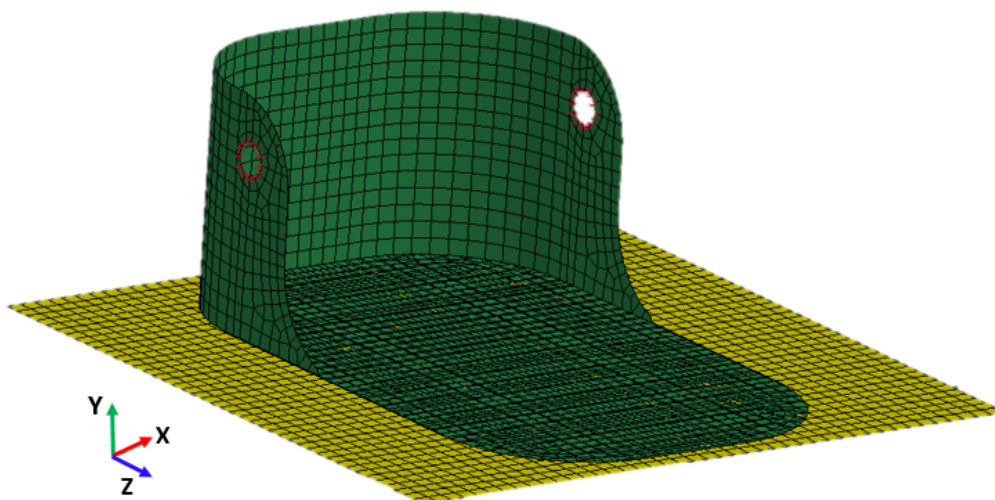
Nós do encastramento destacados a vermelho. Plano rígido para a tração.
